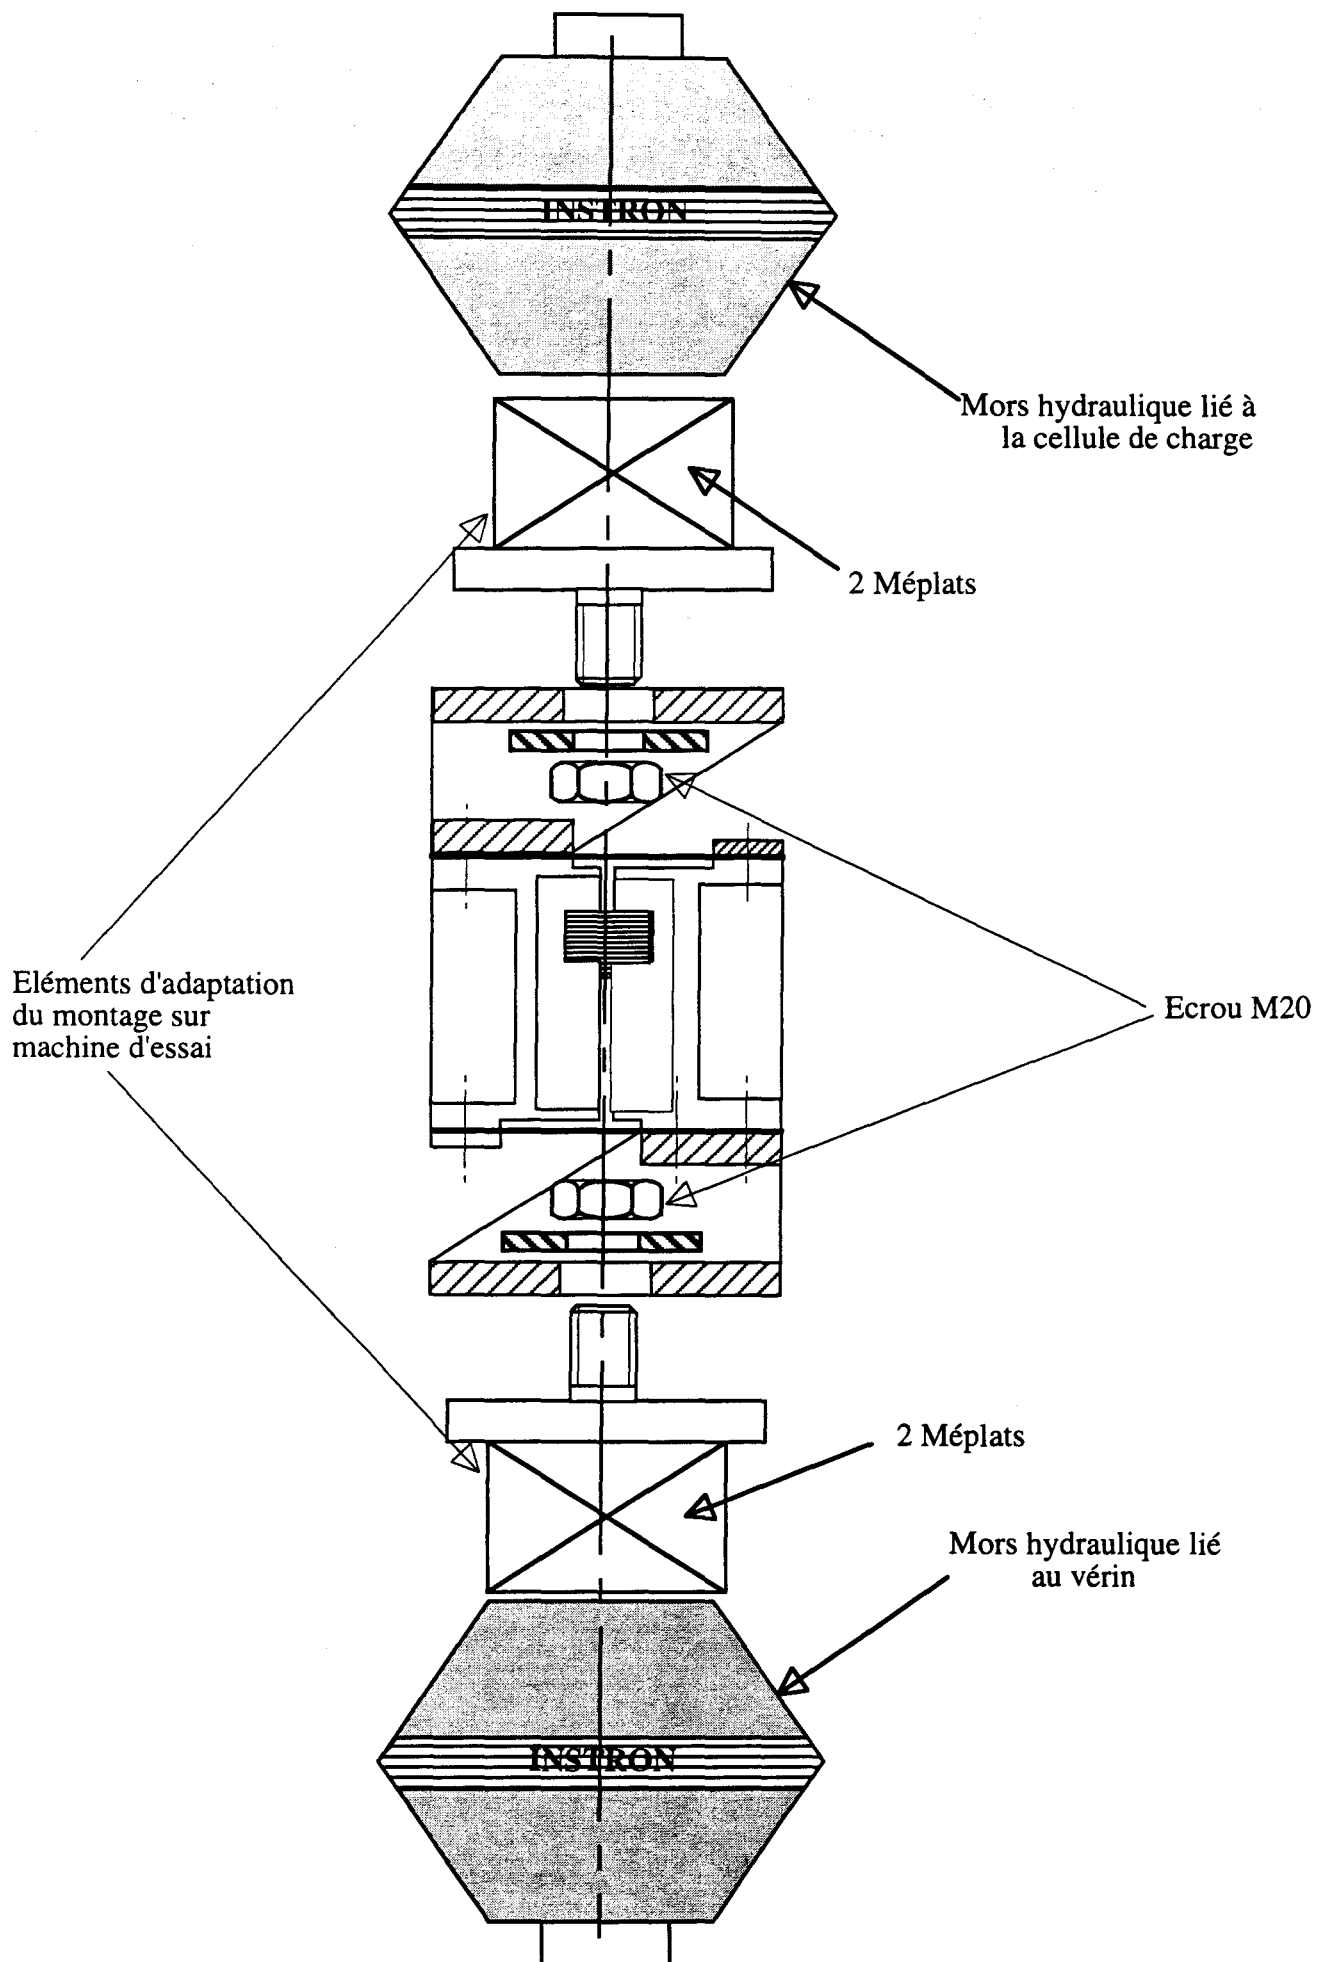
pièces d'adaptation du montage sur la machine d'essai équipée de mors hydraulique (ENSMA)
